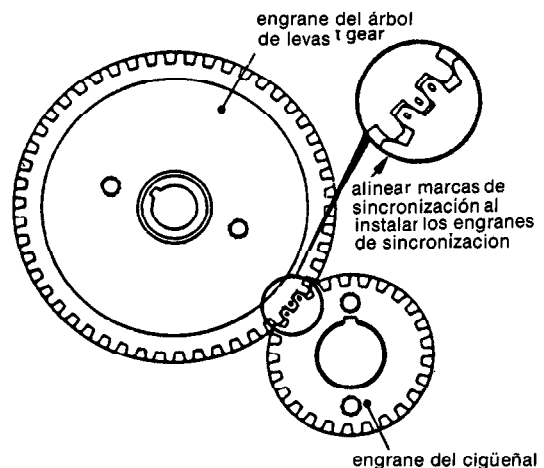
Engranajes del árbol de levas y el cigüeñal. Se muestran las marcas de sincronización en los engranes
